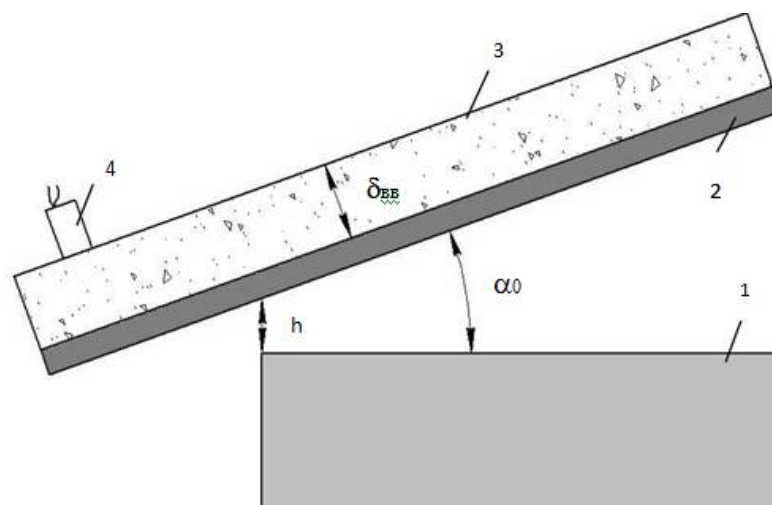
Схема зварювання вибухом: 1 - плакуєма пластина; 2 - пластина плакуюча; 3 – заряд вибухової речовини; 4 – детонатор [4]
